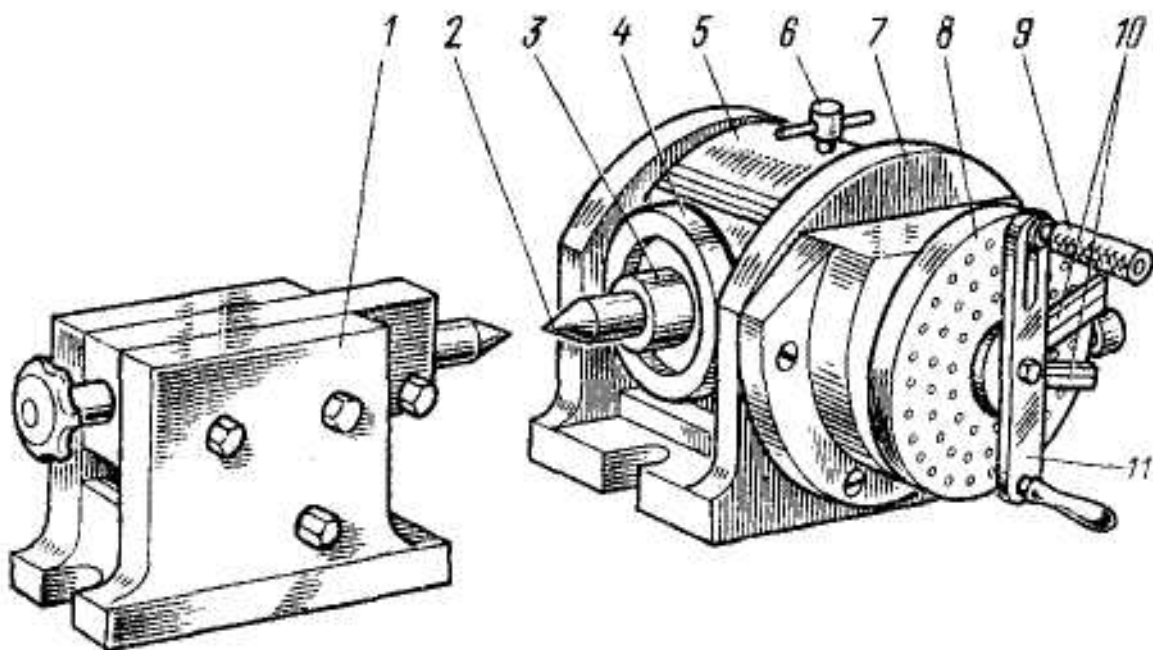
Универсальная делительная головка: 1 – задний центр; 2 – центр головки; 3 – шпиндель; 4 – диск непосредственного деления; 5 – корпус; 6 – стопор; 7 – основание; 8 – делительный диск; 9 – фиксатор; 10 – раздвижной сектор; 11 – рукоятка
